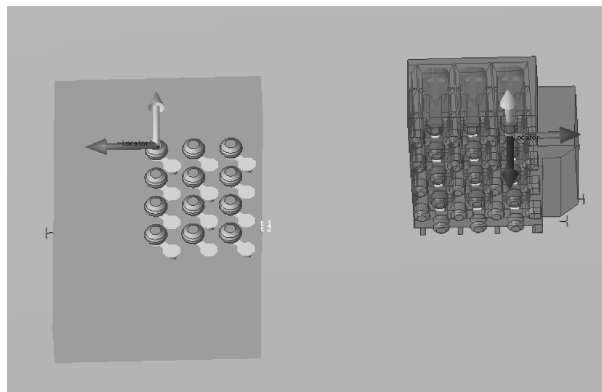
使用 locator 对连接器及 PCB 进行精确定位
